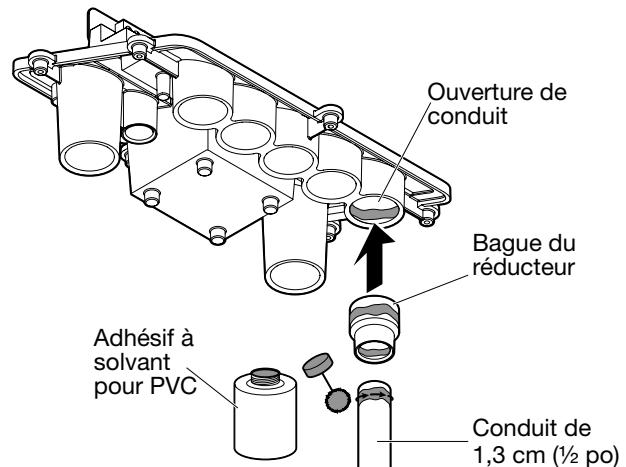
Utilisation d'un conduit de 1,3 cm (1/2 po)
